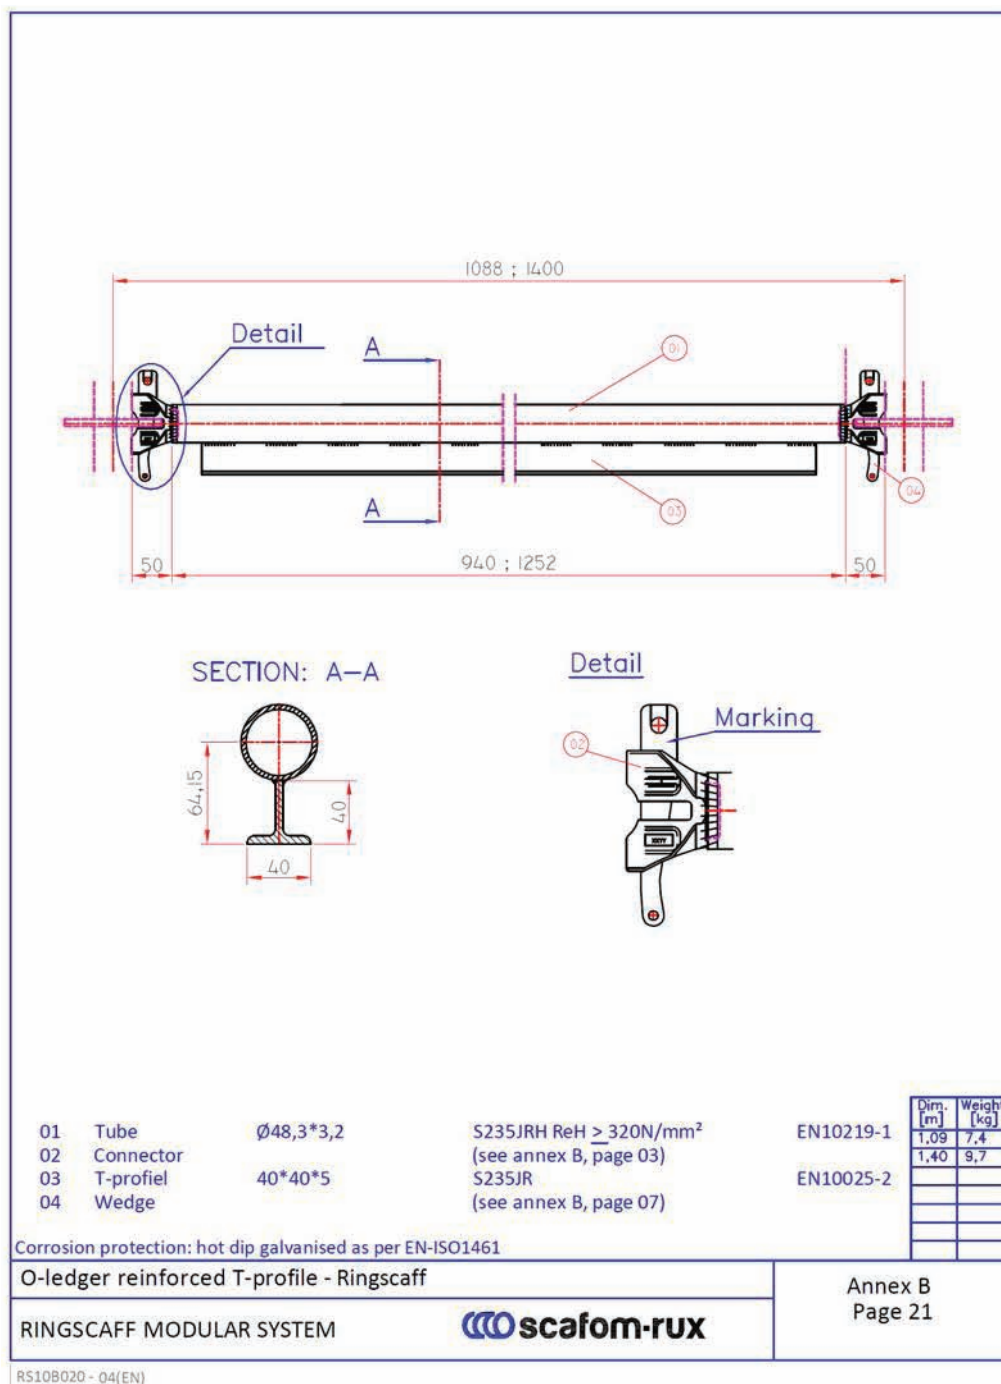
Travessa com secção tubular reforçada com perfil em T
